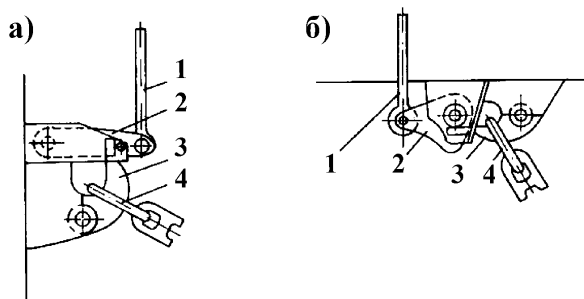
Крепление коренного конца якорной цепи: а – крепление к переборке, б – к крышке цепного ящика; 1 – тяга привода, 2 – рычаг, 3 – гак, 4 – концевое звено
